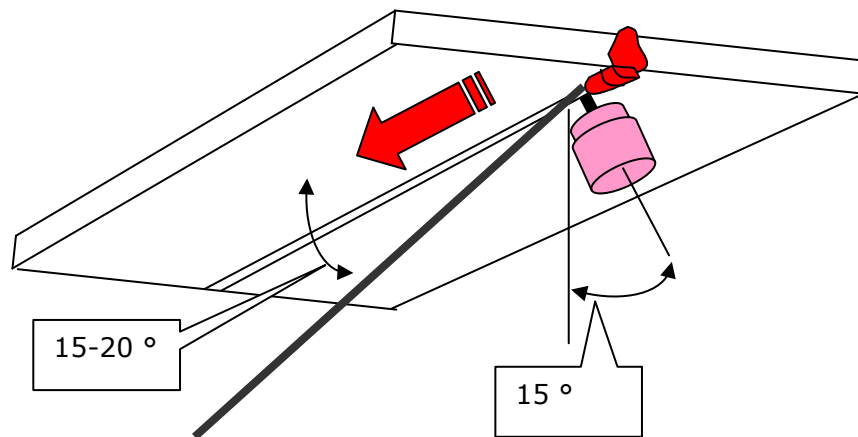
Realización de la soldadura de placas a tope en posición sobre cabeza.
